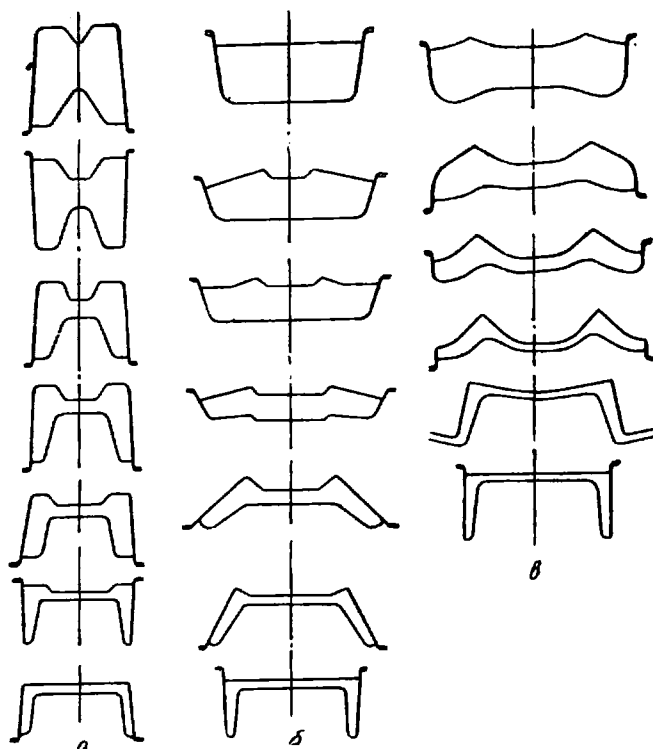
Схемы калибровки валков для прокатки швеллеров
